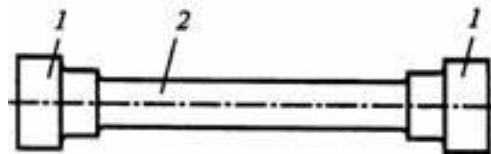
Цилиндрический образец для испытаний на растяжение: 1 – головка; 2 – рабочая часть
